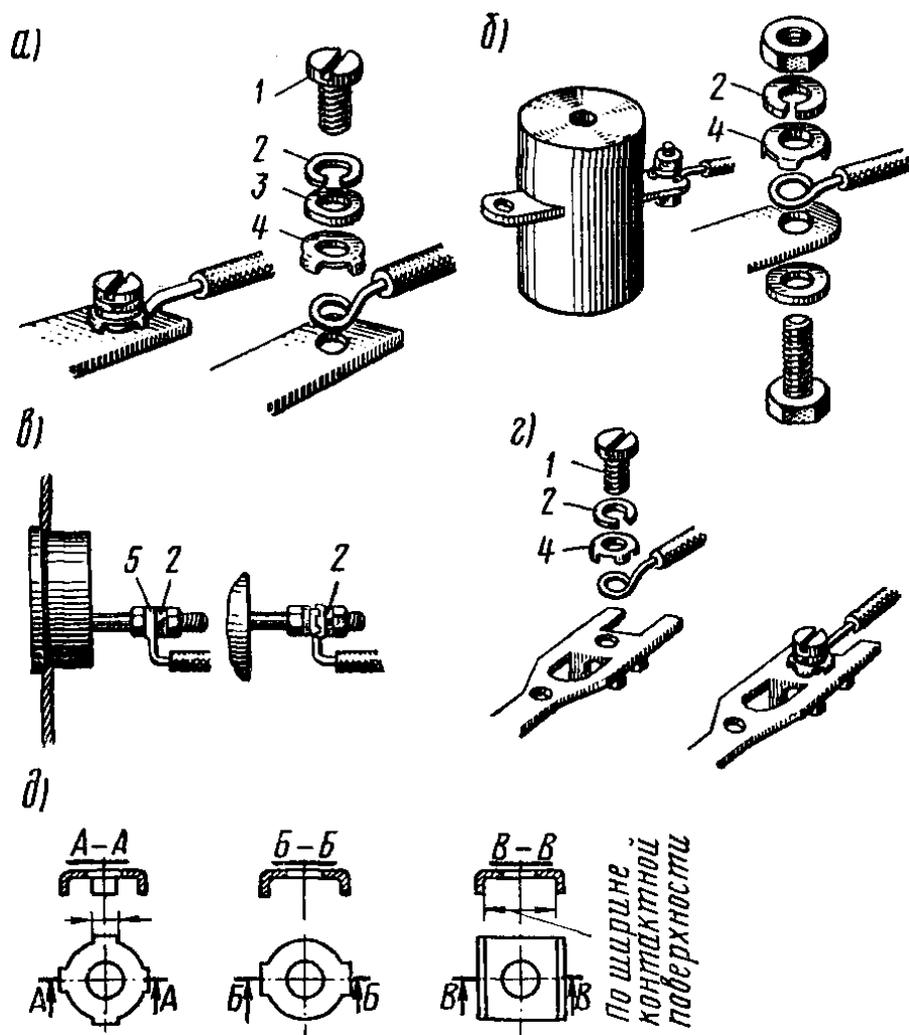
Схемы присоединения (а - д) алюминиевых жил: 1 - винт; 2 - стандартная пружинная шайба; 3 - плоская шайба; 4 - ограничивающая шайба-звездочка; 5 - жила, опрессованная в пистоне
